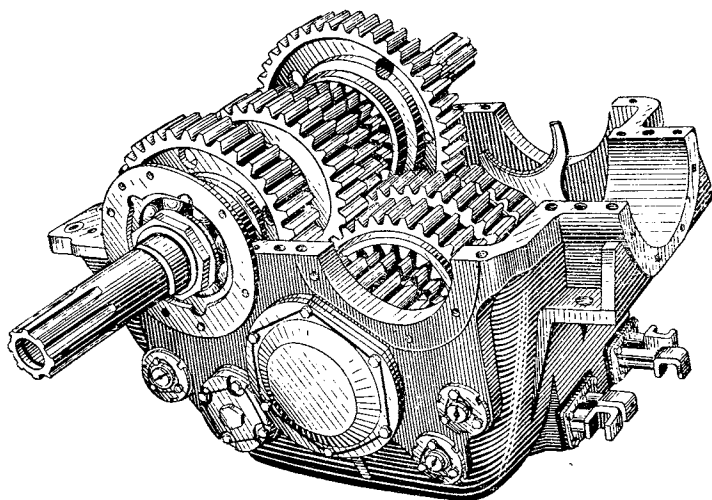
Коробка передач со снятой верхней половиной картера и вынутыми ведущим и ведомым валами
